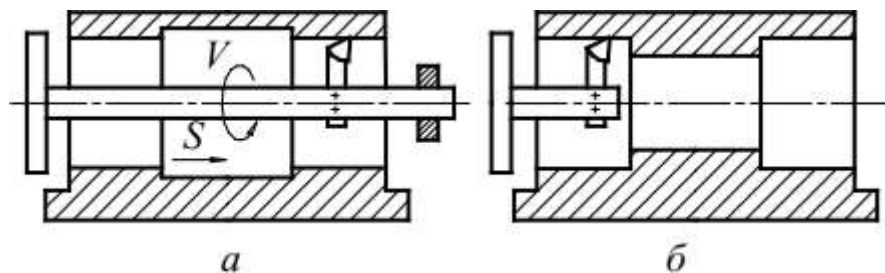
Конструкція корпусних деталей зі співвісними отворами:
